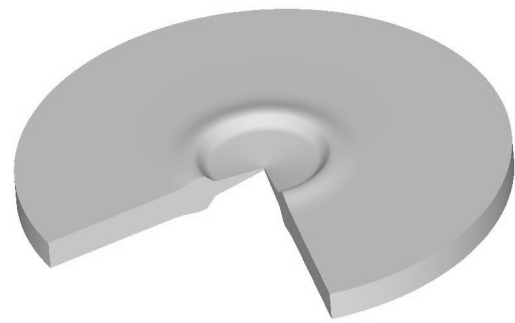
Здеформована заготовка в розрізі після видавлювання
